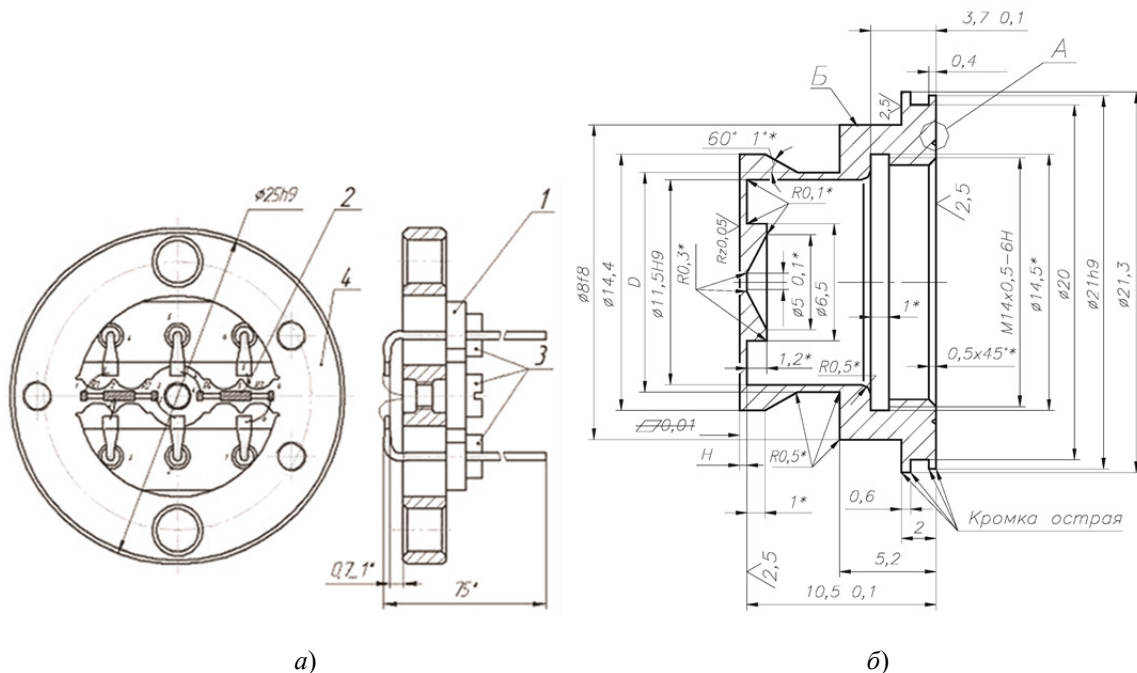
Конструкции узлов и деталей металлопленочного датчика давления:
